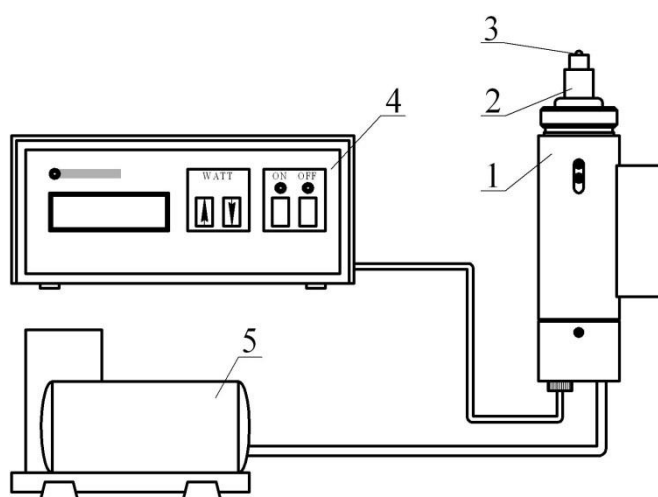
Схема ультразвукового комплекса: 1 – корпус преобразователя для закрепления на станке; 2 – волновод; 3 – индентор; 4 – генератор; 5 – компрессор
